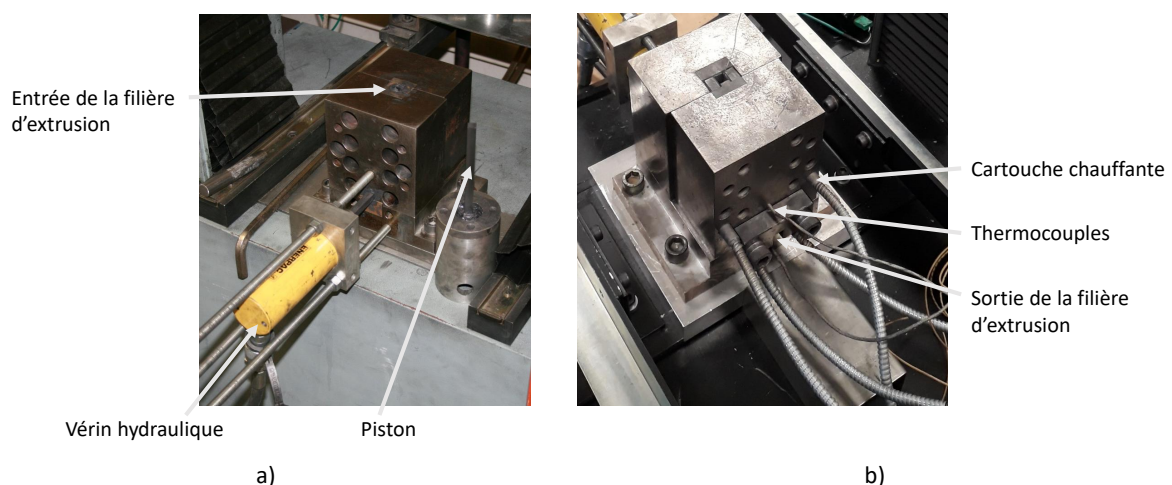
Dispositif ECAP monté sur la machine a) vu de l'avant avec le piston qui s'introduit dans le dispositif b) vu de l'arrière
